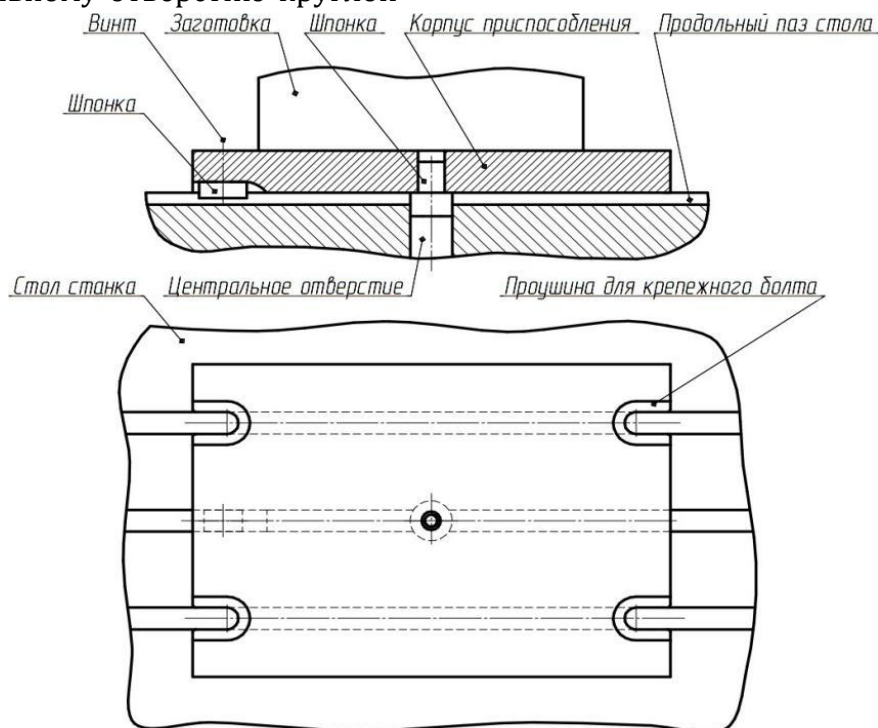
Базирование приспособления на столе станка по шпонкам,
